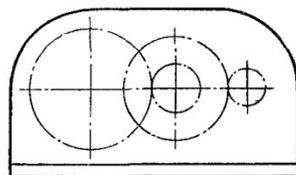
Двухступенчатый редуктор с цилиндрическими зубчатыми колесами
